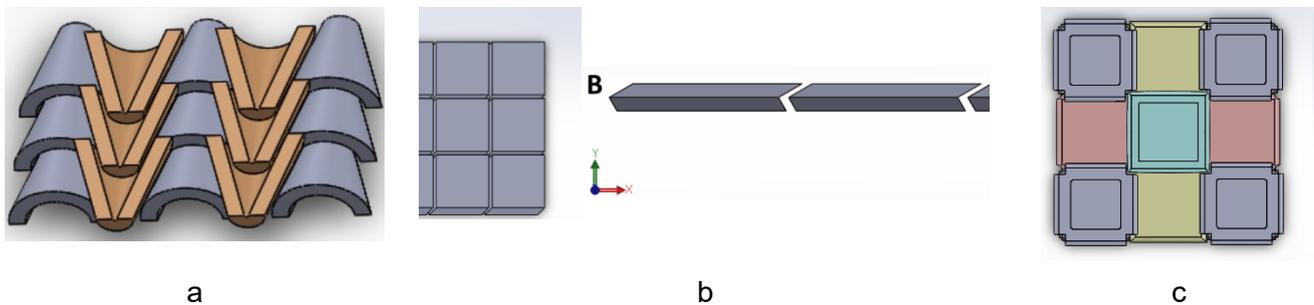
Ansicht von drei Baugruppen: a) doppelagige Tunnelstruktur; b) flache quadratische Struktur mit Fugen; c) Variante einer flachen Struktur mit Gelenken.
